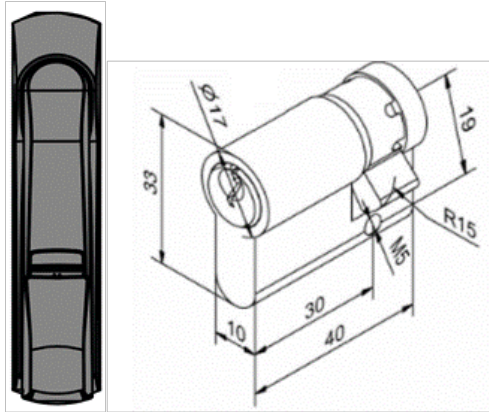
Drehriegelverschluss und Schließzylinder (Abmessungen in mm)
